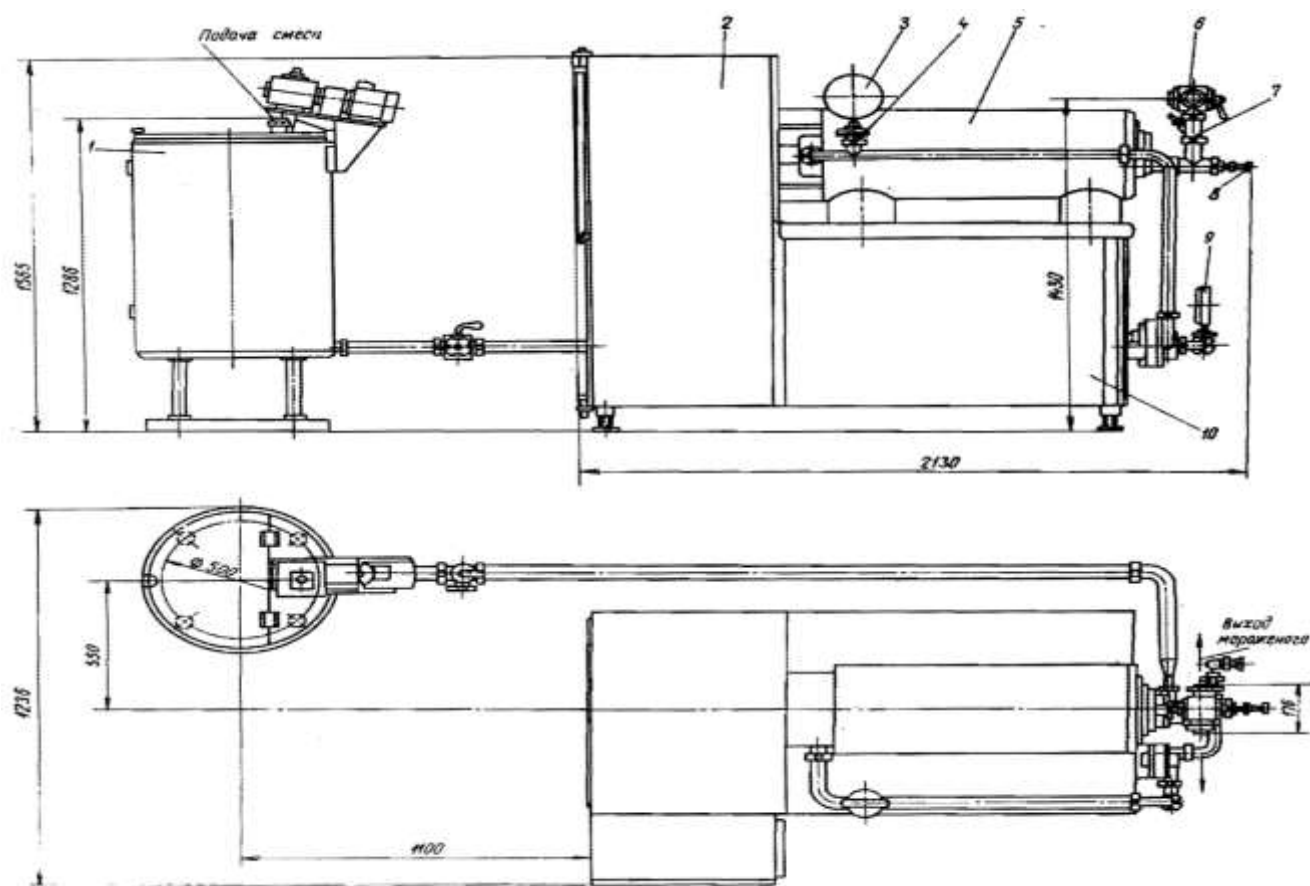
Общий вид фризера марки Б6-ОФШ для мороженого:
